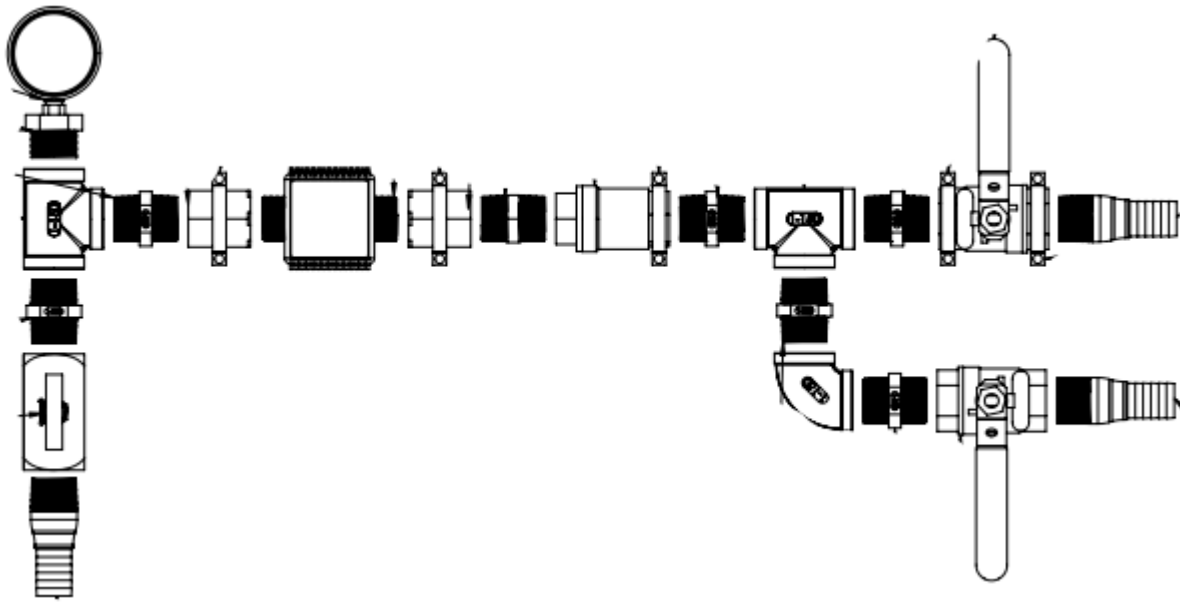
Construcción del mezclador estático, Fuente Propia.
